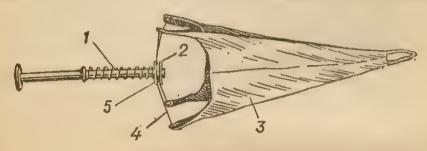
Стабилизатор: 7 — пружина; 2 — втулка; 3 — матерчатый конус; 4 — проволочное перо; б - кольцо
